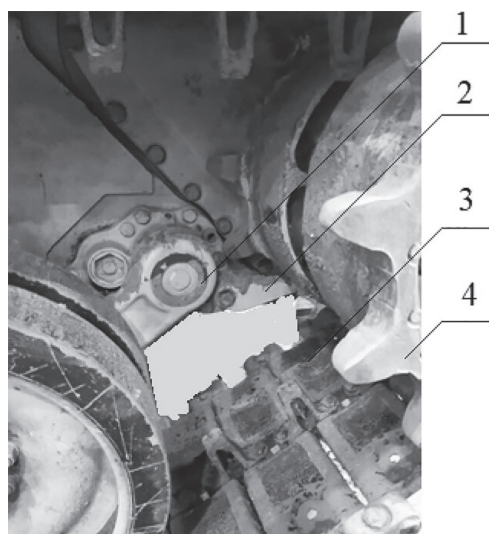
Регулирование модальных характеристик наклонной ветви гусеничного движителя введением успокоителя жестко закрепленного на корпусе машины: 1 — верхняя головка балансира; 2 — «нож» для очистки ведущего колеса; 3 — гусеница; 4 — зубчатый венец ведущего колеса
